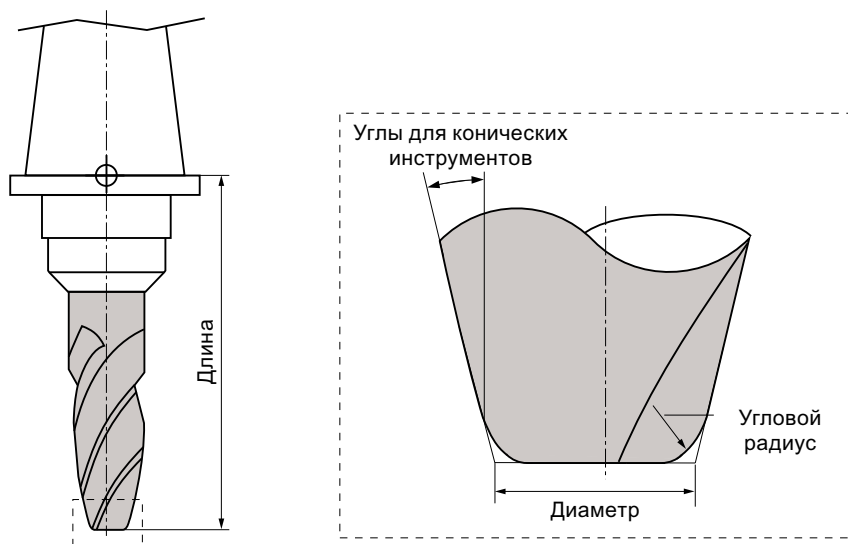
Инструмент 3D на примере конической фрезы с закруглением углов (тип 156)
